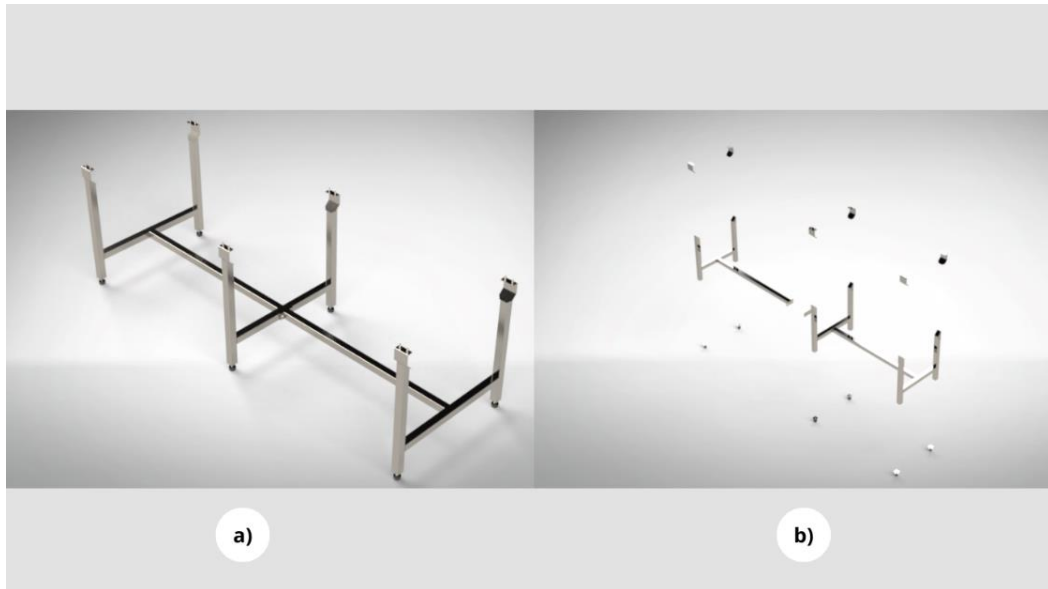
Estrutura inferior - a) vista em conjunto e b) vista explodida
